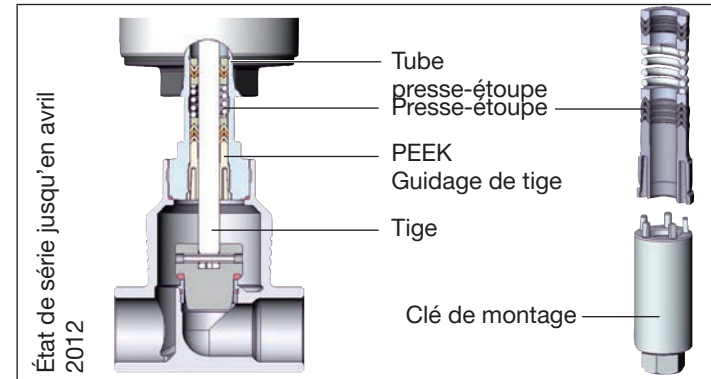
Remplacement du presse-étoupe (PEEK guidage de tige)
